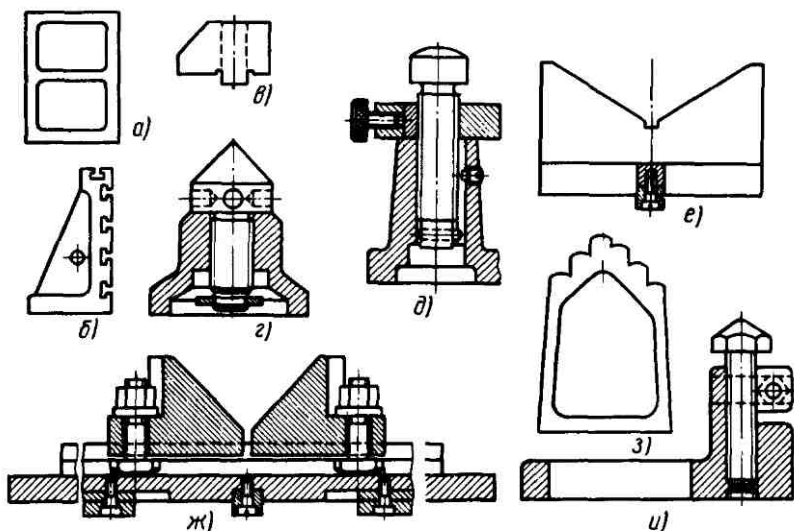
Принадлежности для установки и закрепления обрабатываемых деталей
